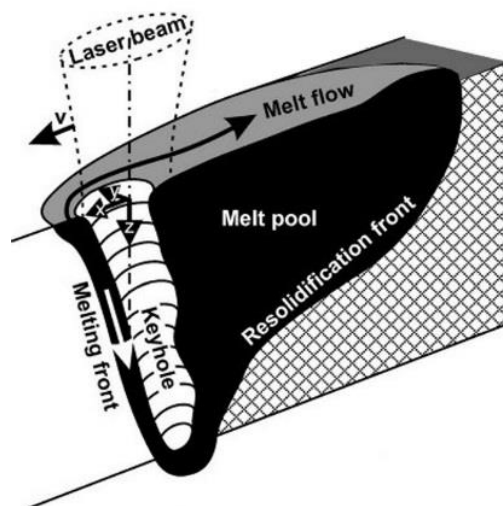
схема парогазового канала при лазерной сварке с кинжальным проплавлением [9].
